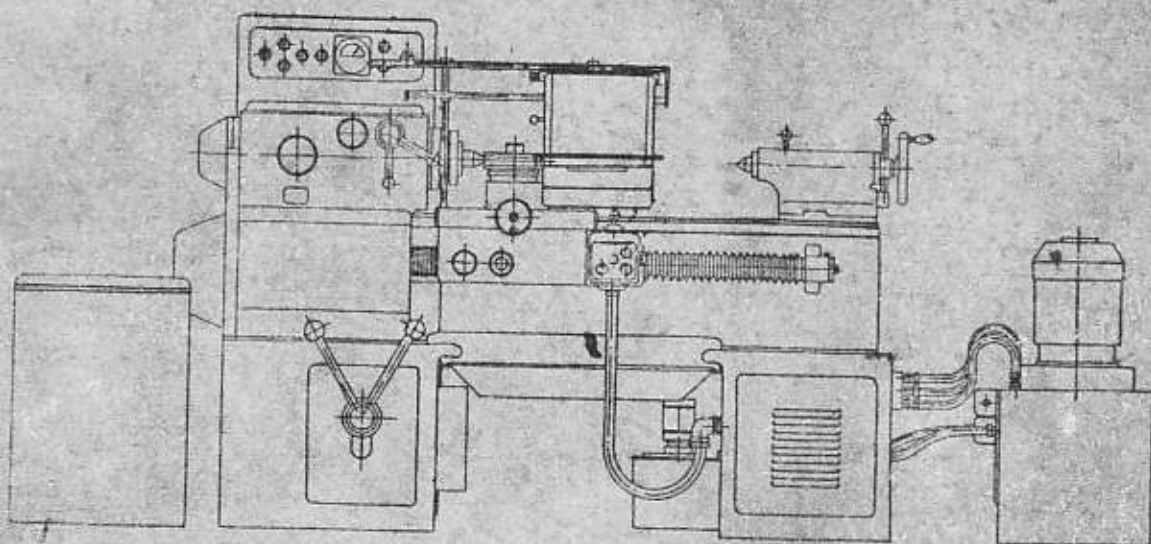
ОБЩИЙ ВИД СТАНКА.
